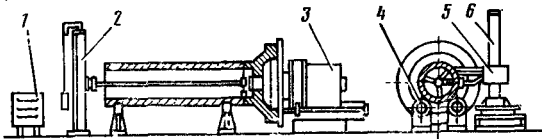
Типовая установка для сборки и электрошлаковой сварки кольцевых швов цилиндрических конструкций:
